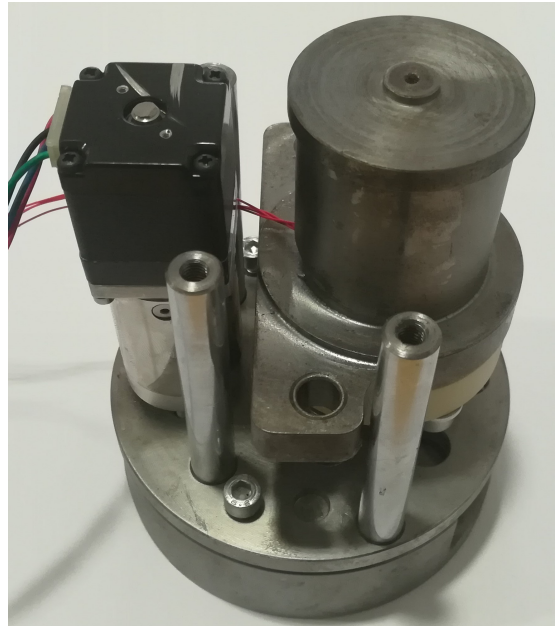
Montagem do conjunto 1 com o conjunto 3.
